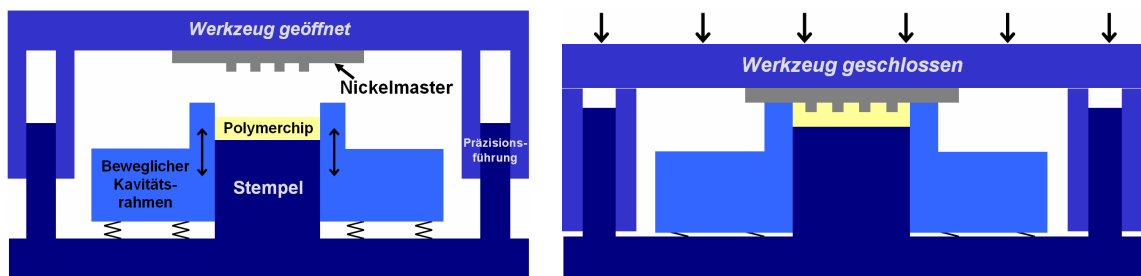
Prinzipskizze des Spezial-Heißprägewerkzeugs
